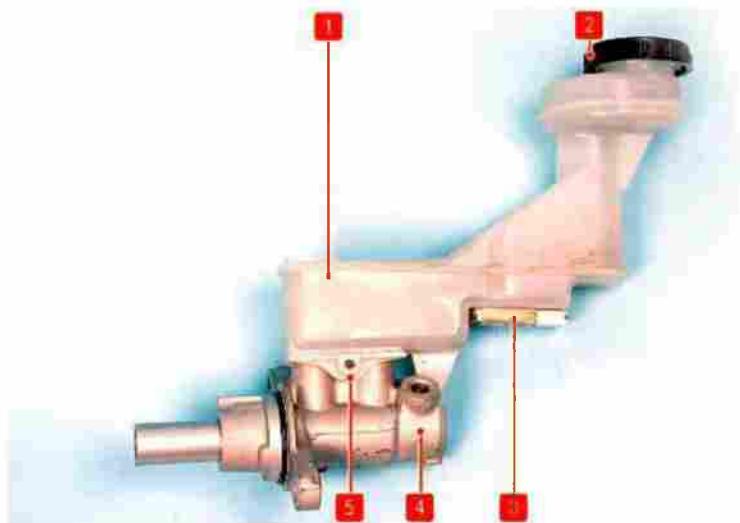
Главный тормозной цилиндр: 1 – бачок главного тормозного цилиндра; 2 – пробка бачка главного тормозного цилиндра; 3 – датчик уровня тормозной жидкости; 4 – главный тормозной цилиндр; 5 – фиксатор бачка.
